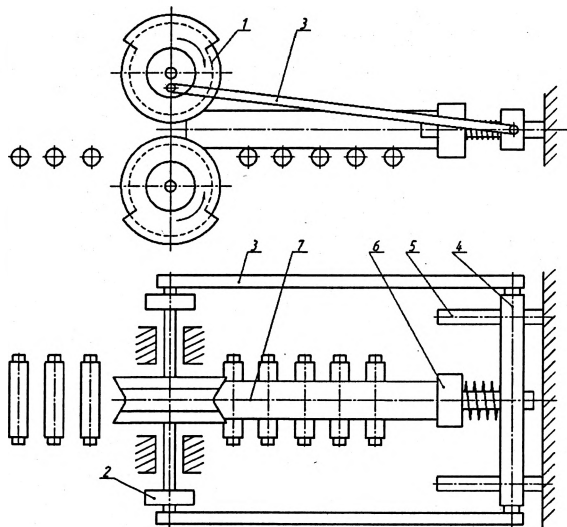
Схема стана 2198 для вальцовки заготовки передней балки
